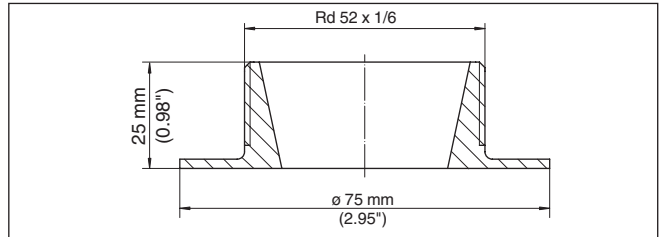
Maße Einschweißstutzen Konusanschluss DN 25
